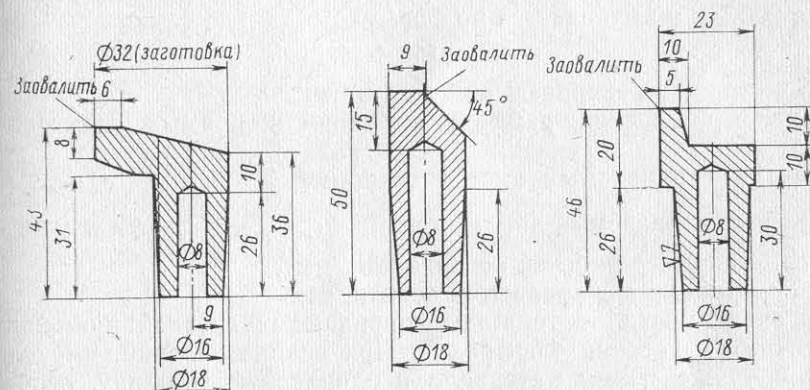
Электроды для сварки в труднодоступных местах.
